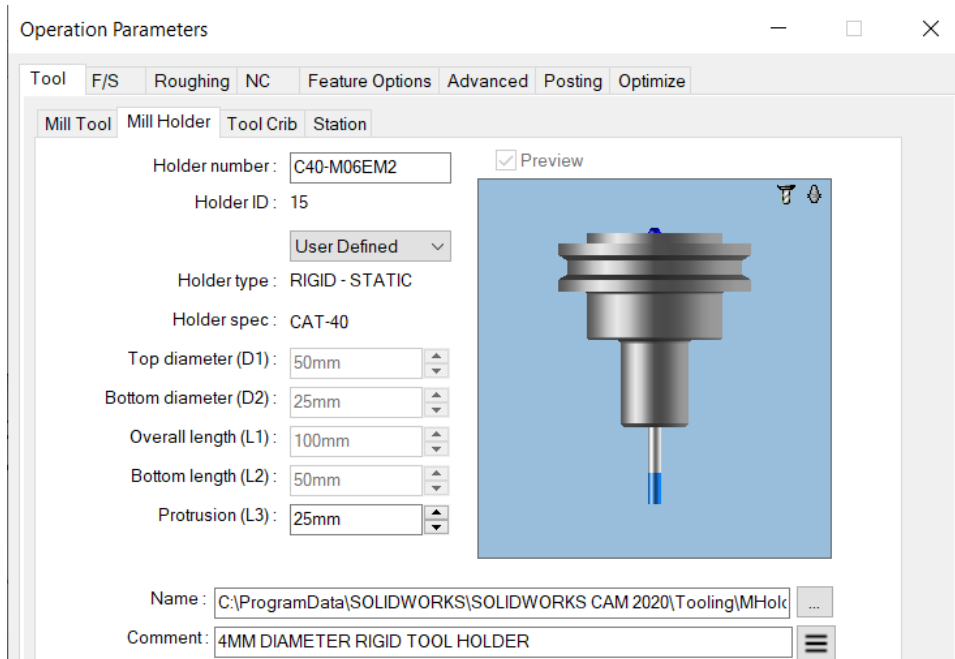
Державка фрези 4MM DIAMETER RIGID TOOL HOLDER.
